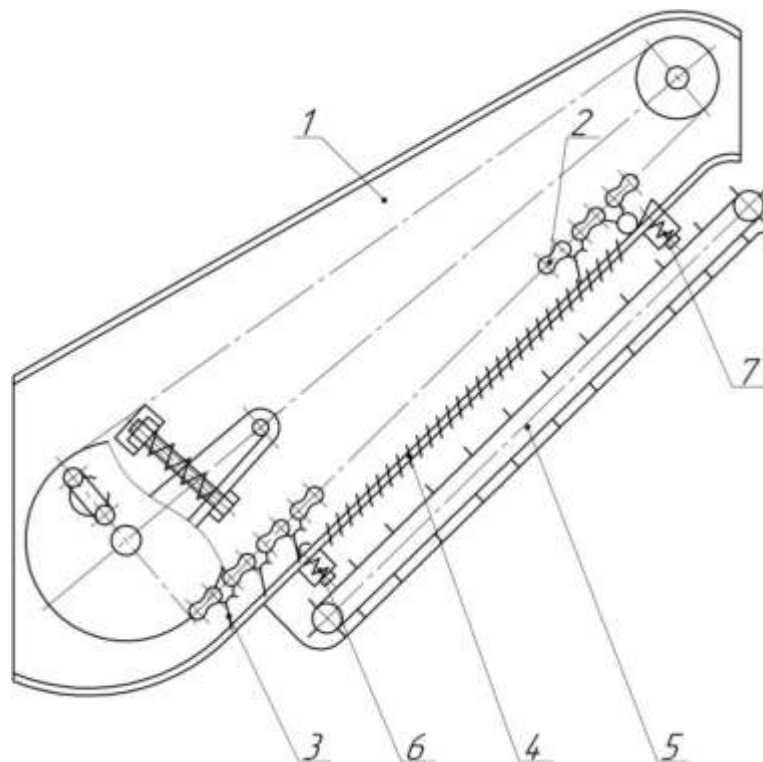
Наклонная камера зерноуборочного комбайна (SU авторское свидетельство № 1687078): 1 – корпус; 2 – плавающий транспортер; 3 – скребки; 4 – решетчатое днище; 5 – устройство для отвода свободного зерна; 6, 7 – механизм очистки решетчатого днища
